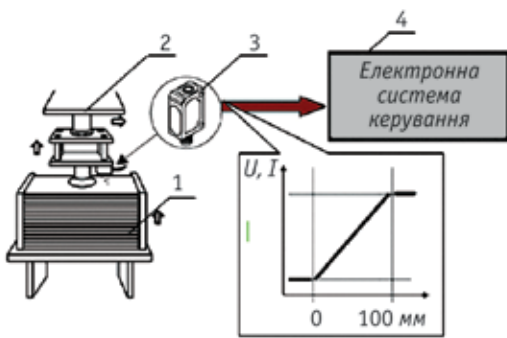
Принципова схема використання оптичного датчика в модулі виділення заготовки упаковки: 1 – магазин упаковок, 2 – захоплювальний пристрій з механізмом вертикального переміщення, 3 – оптичний датчик, 4 – електронна система керування
